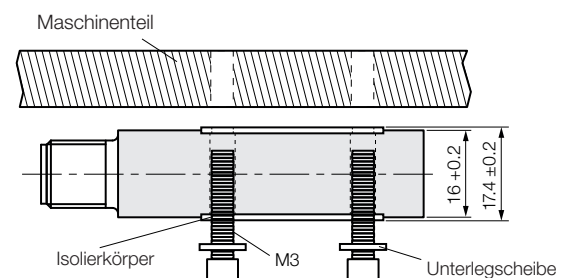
Sensorkopf mit Isolierkörper montieren
